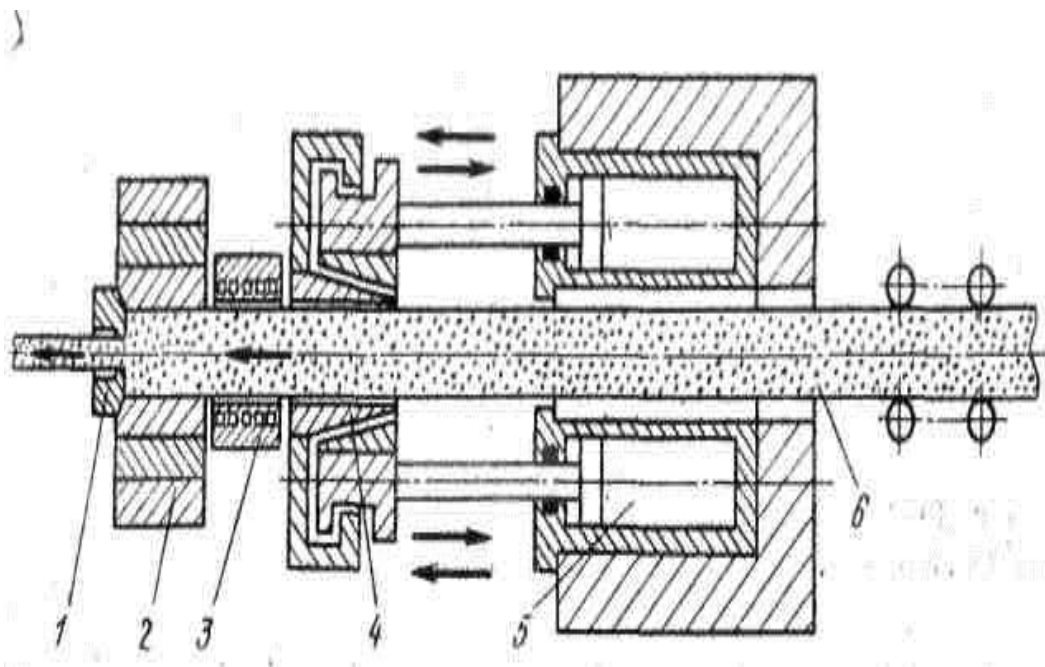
Схема агрегату для безперервного пресування литої заготовки необмеженої довжини:
